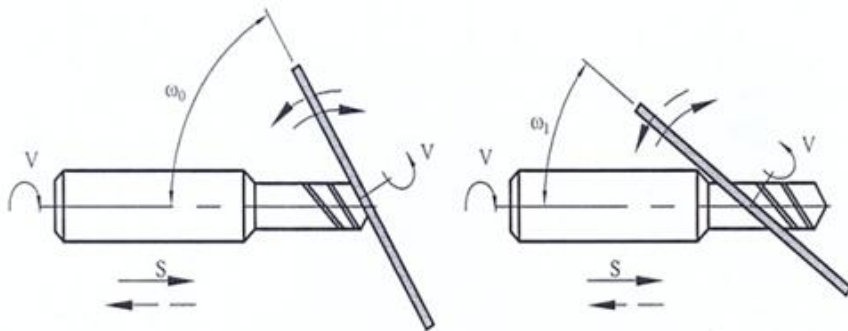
Схема изменения ориентации осей заготовки сверла и шлифовального круга методом поворота оси шлифовального шпинделя.
